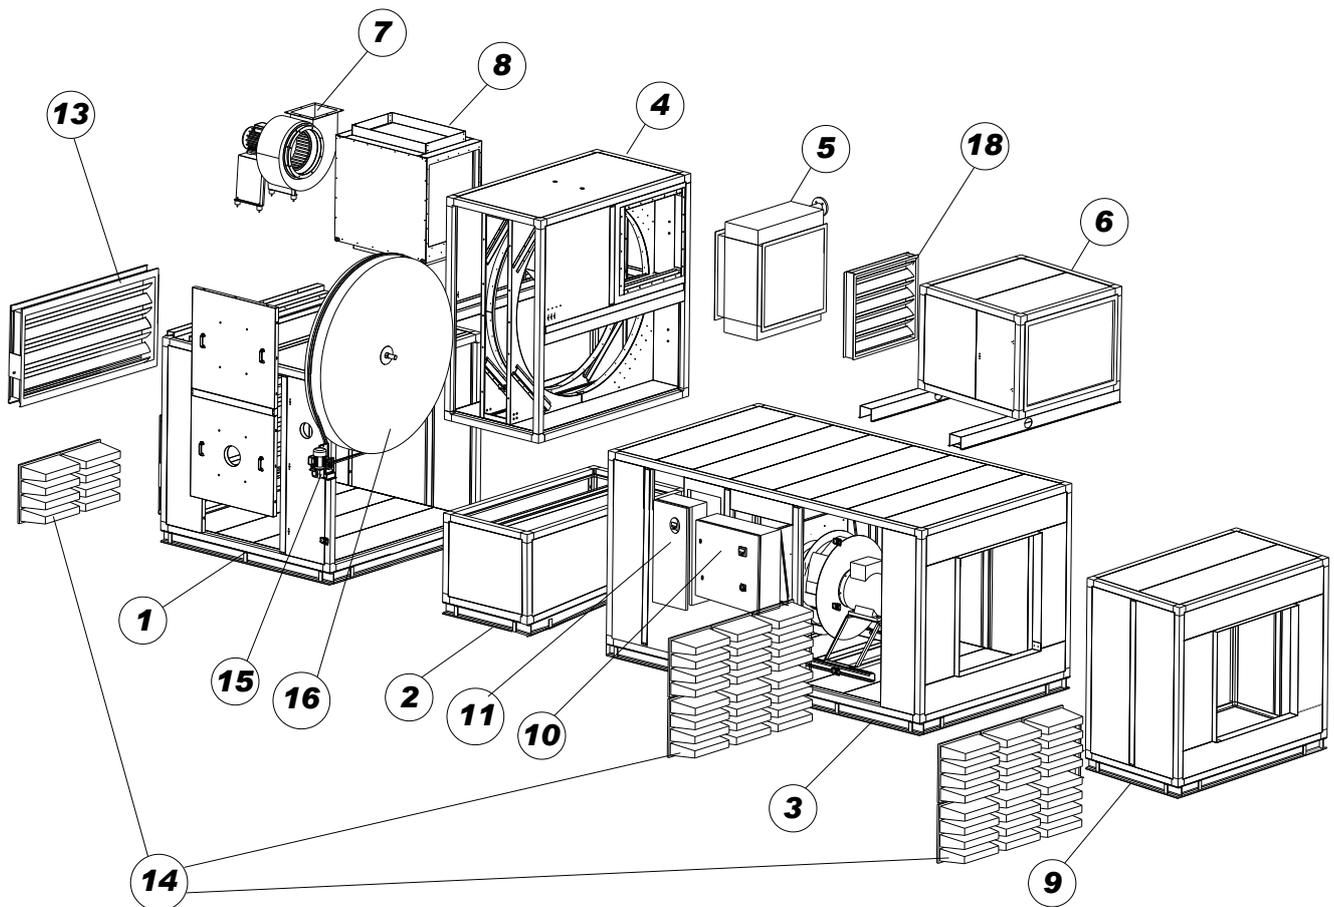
Explosionszeichnung der Hauptkomponenten für die Baureihe DFLEX
